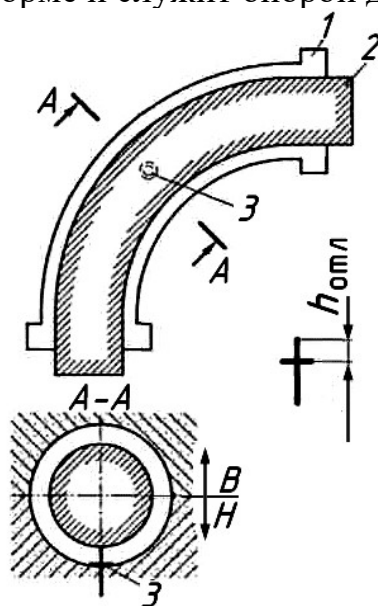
Фиксация стержня отливки патрубка жеребейкой: а – стержень, установленный в форму с использованием жеребейки; б – схематическое изображение жеребейки; 1 – отливка; 2 – стержень; 3 – жеребейка; $h_{отл}$ – толщина стенки отливки; В, Н – верх и низ формы
